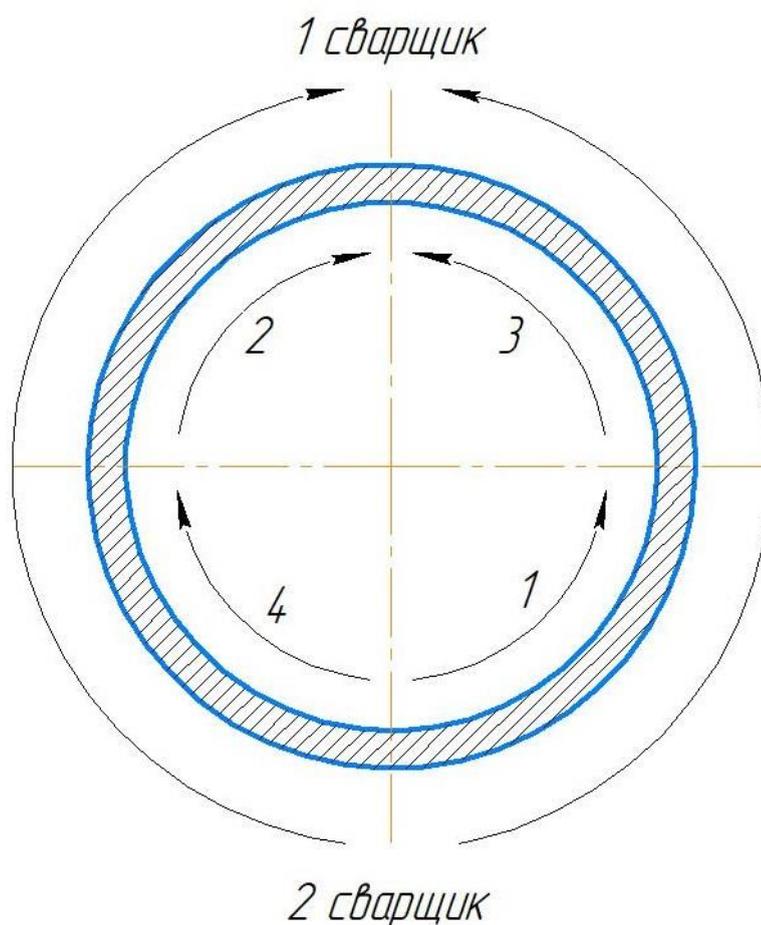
Схема сварки двумя сварщиками вертикального стыка трубы, где 1- 4 - последовательность наложения сварного шва
